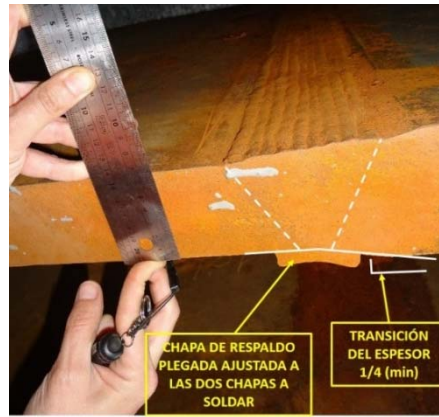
Chapa de respaldo plegada en soldadura de chapas con diferente espesor
